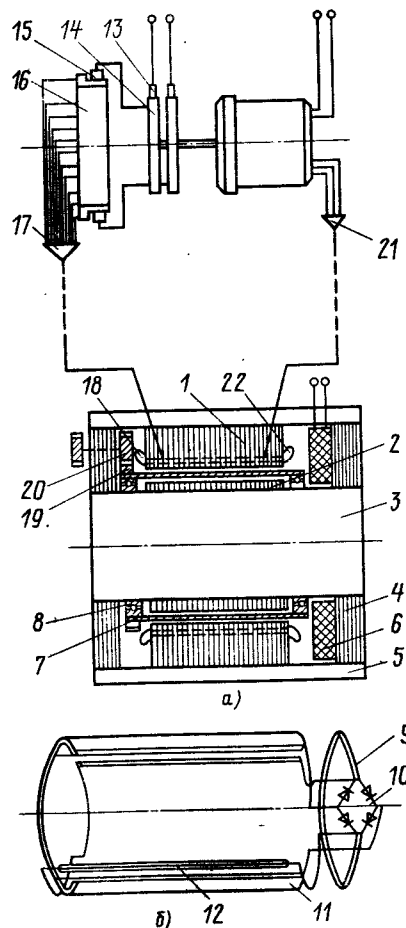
Схема конструкции двигателя. а — продольный разрез и схема соединений; б — электрическая схема обмотки ротора
